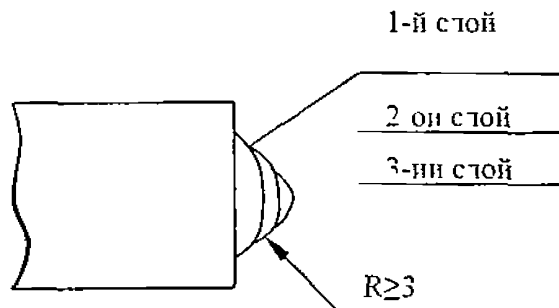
Взаимное расположение валиков при сварке
